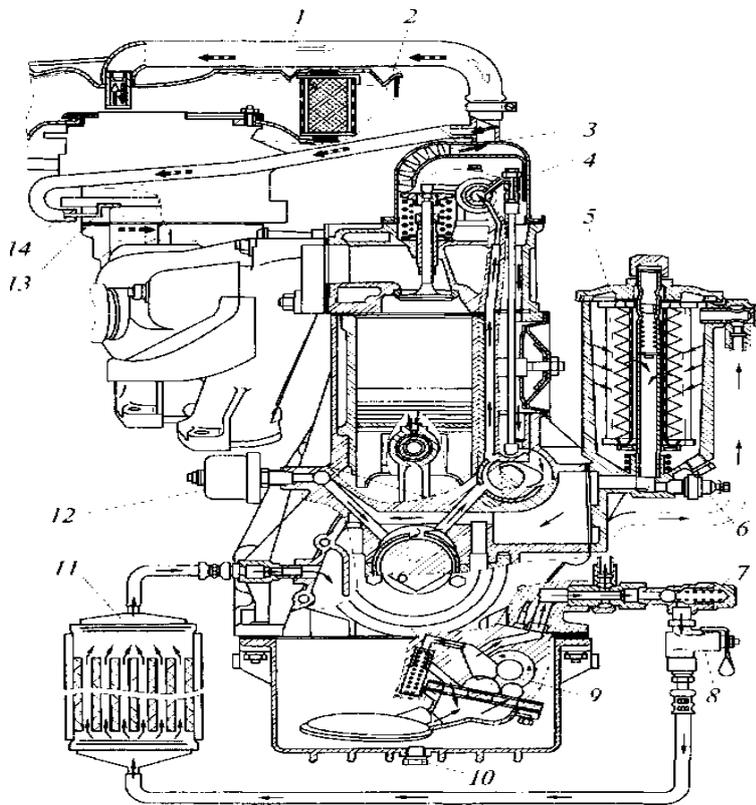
Смазочная система и система вентиляции картера двигателя ГАЗ-31029:
